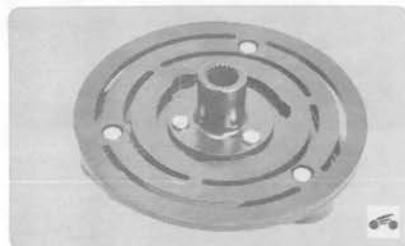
Универсальное приспособление для фиксации ротора компрессора
